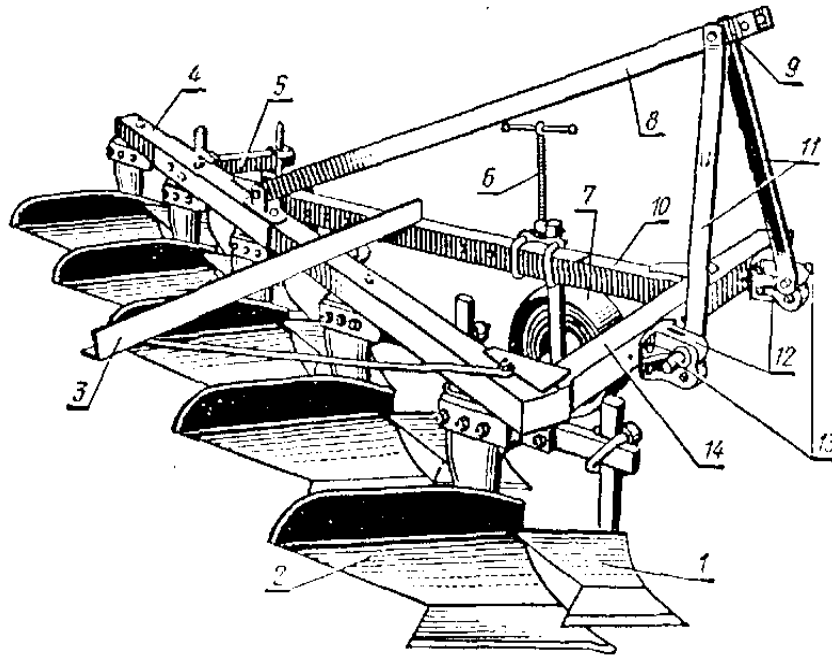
Навесной пятикорпусный плуг ПЛН-5-35:
